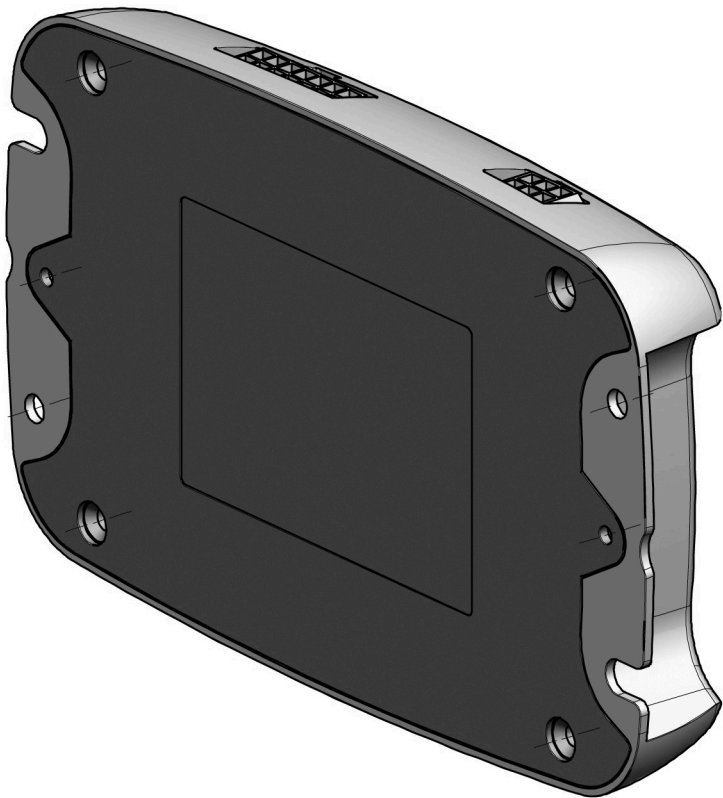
Внешний вид нижней панели корпуса основного блока.
